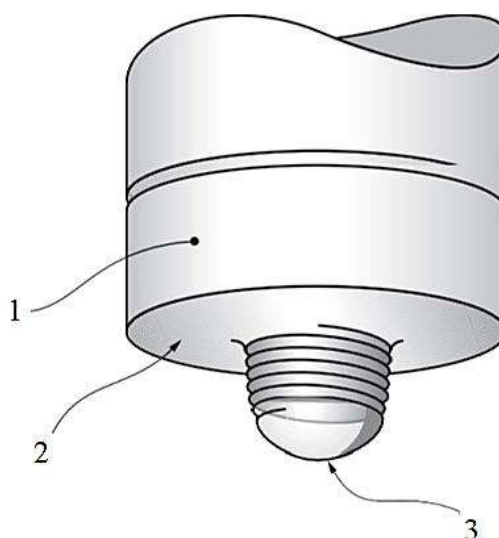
Инструмент для сварки трением с перемешиванием [15]:
